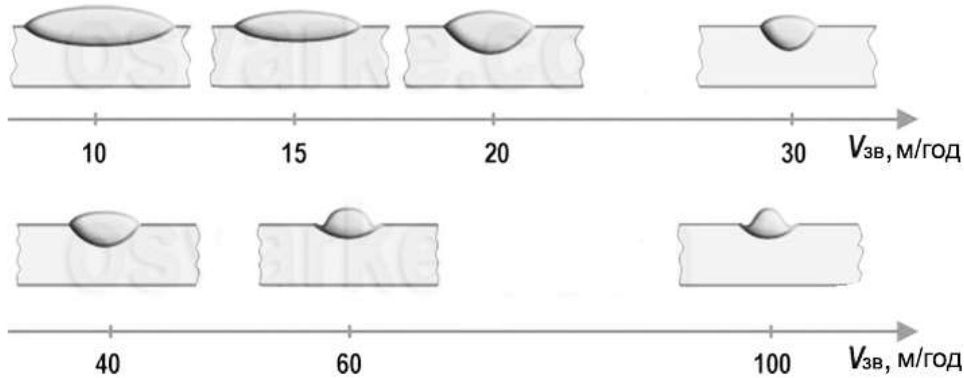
Вплив швидкості зварювання на форму й розміри шва
